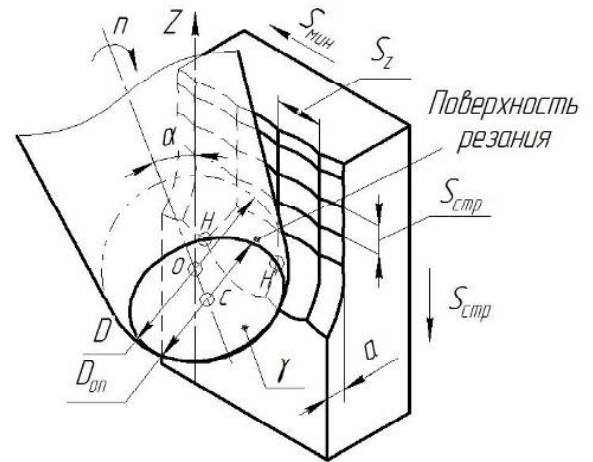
Схема финишного фрезерования ТЭ детали сферической концевой фрезой:
